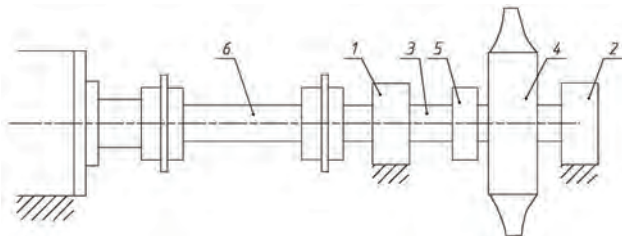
Компоновка ротора: 1 – радиальная подшипниковая опора; 2 – радиально-упорная подшипниковая опора; 3 – коренной вал ротора; 4 – РК; 5 – исполнительный механизм поворота лопаток РК; 6 – трансмиссионный вал
